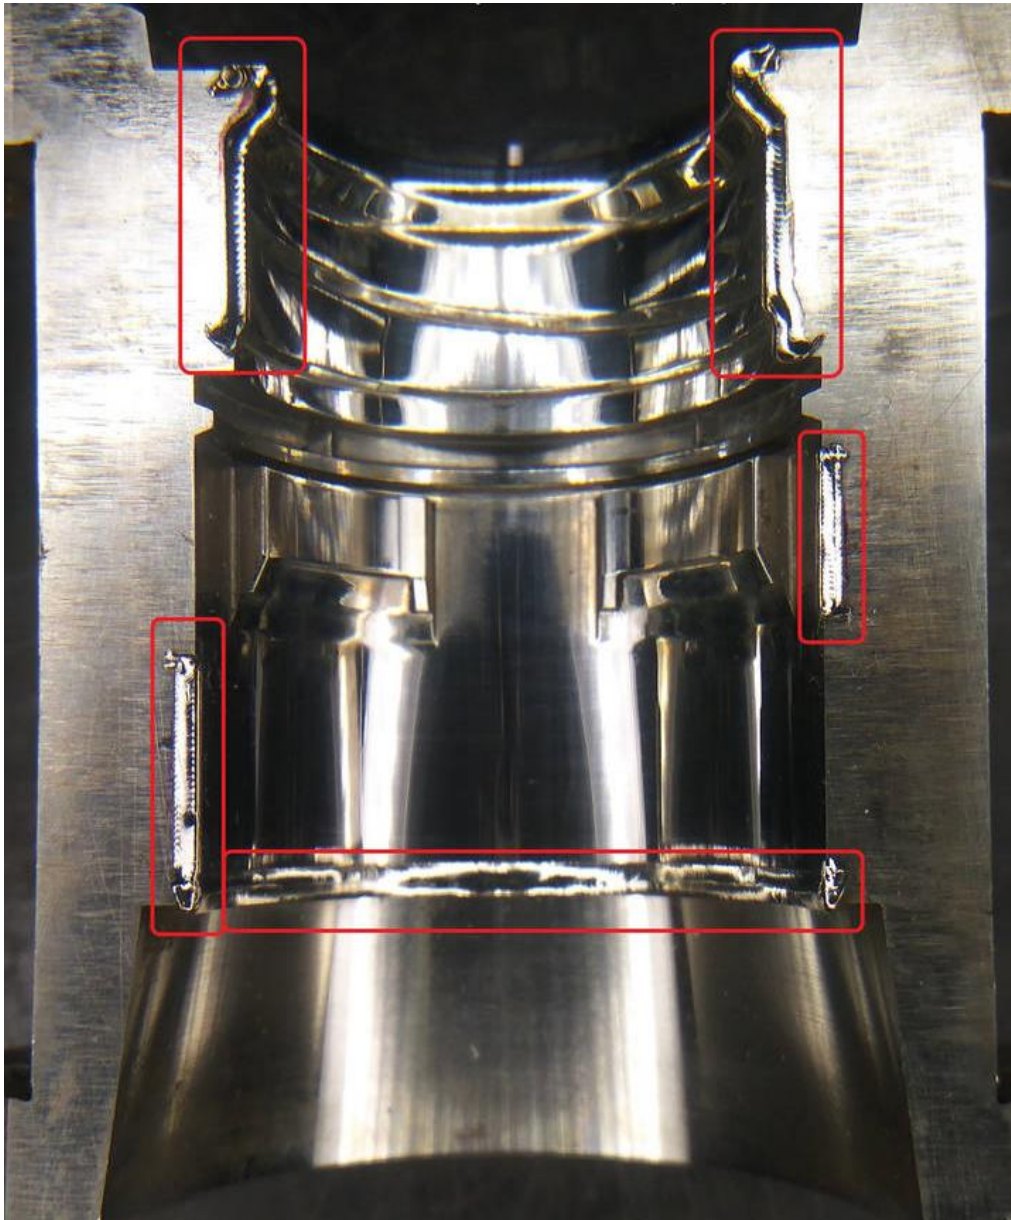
Ремонт прес-форми лазерним наплавленням[3]
